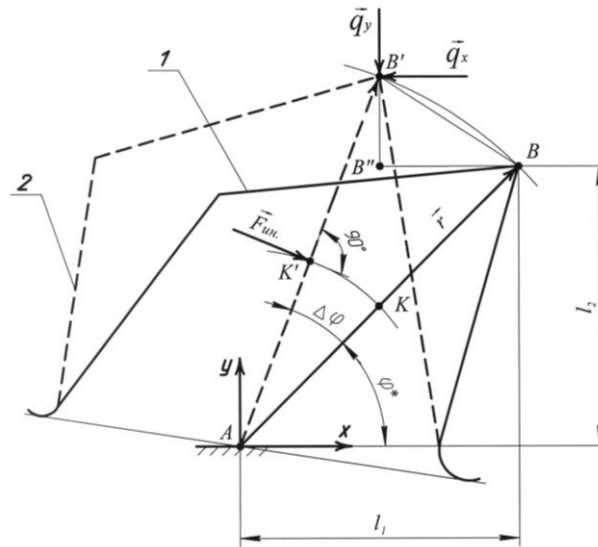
Расчетная схема нагружения режущего зуба прошивки силами, возникающими в процессе резания:
